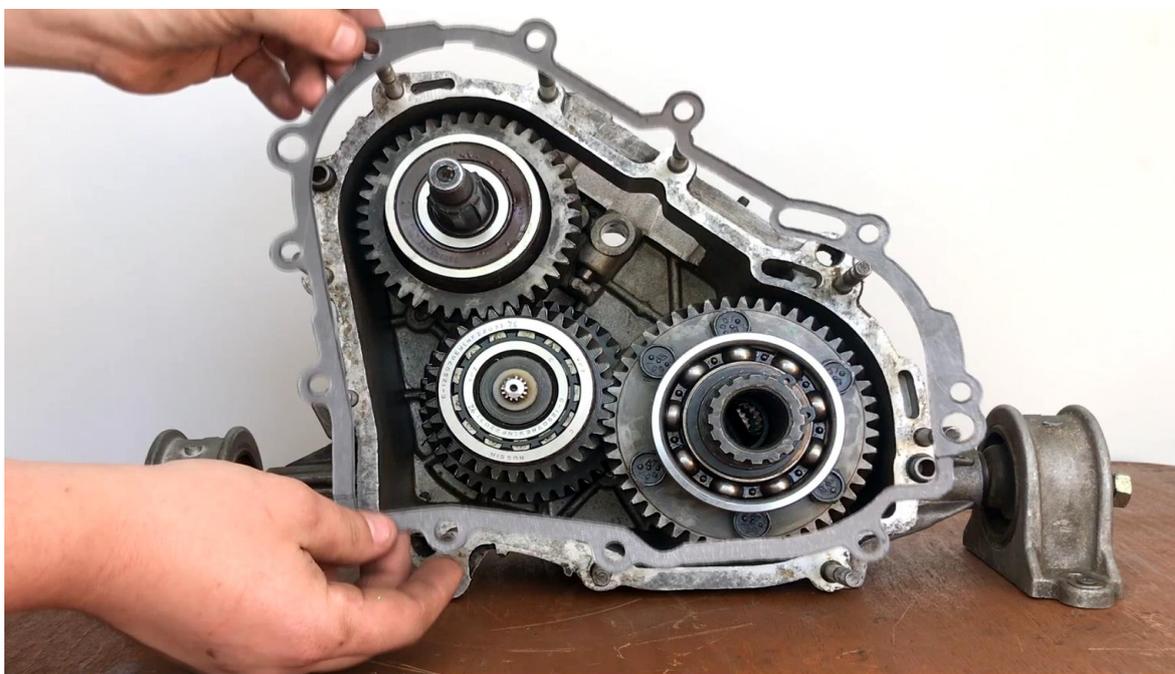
Скриншот видеоролика с выполнением сборки раздаточной коробки автомобиля ВАЗ-2123
